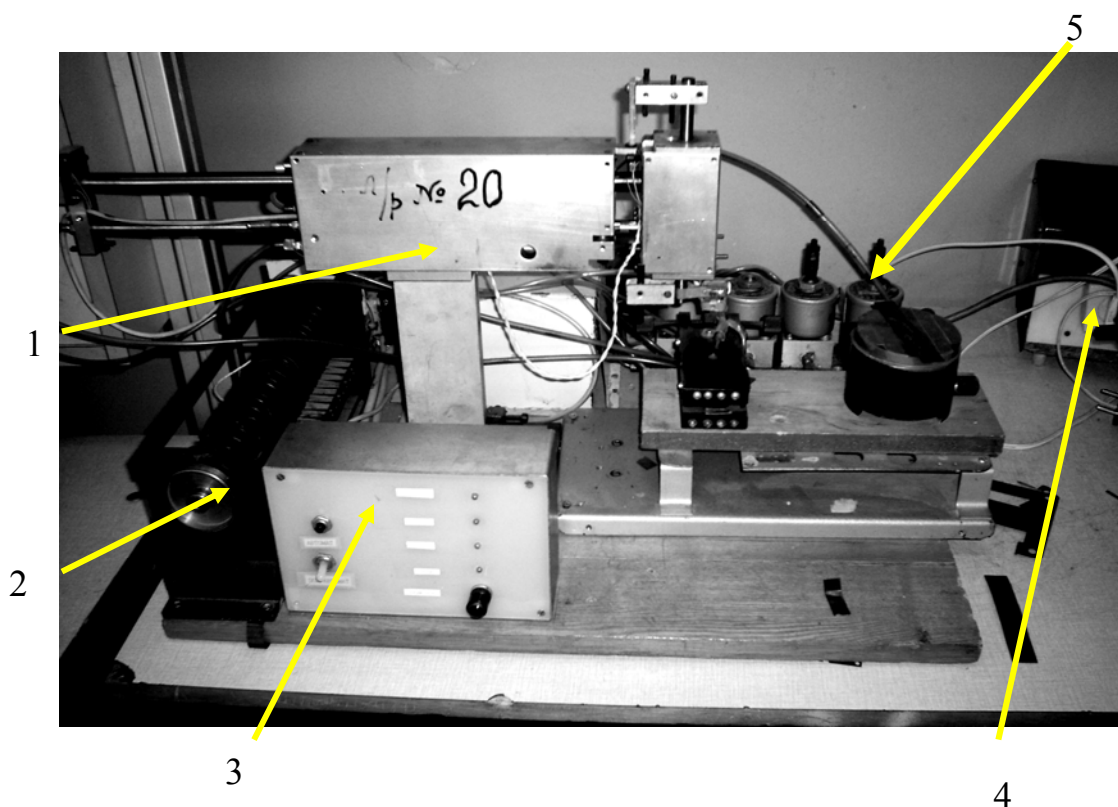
Общий вид установки для автоматической загрузки деталей
